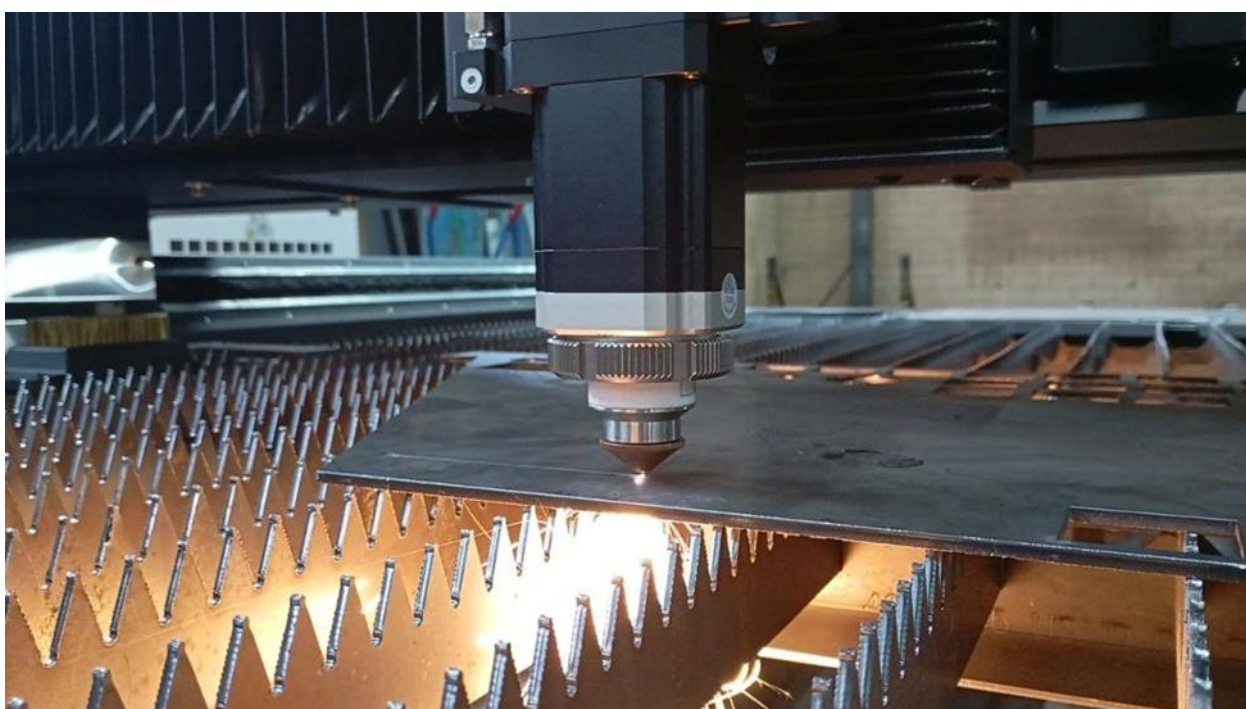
Процес газолазерного різання на верстаті моделі AFX-PRO-12000-1530LD
